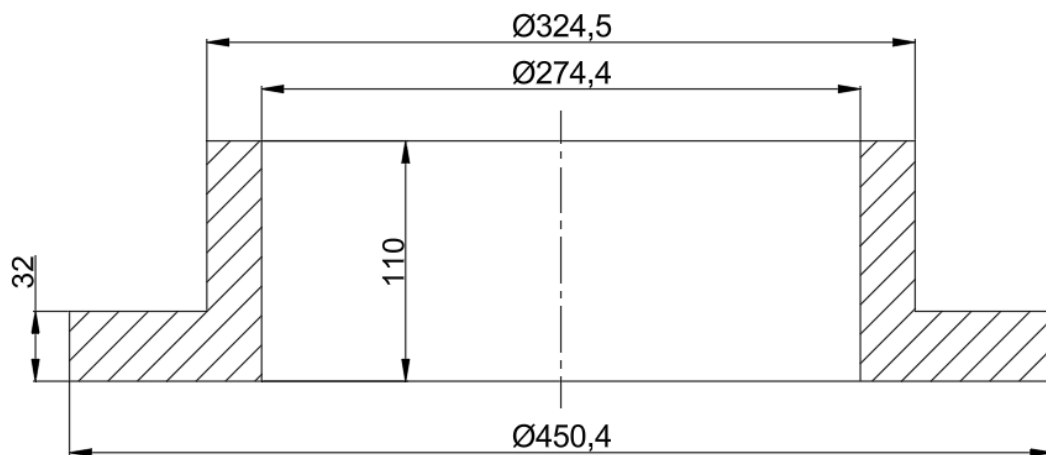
Ескіз заготовки кришки підшипникового вузла
